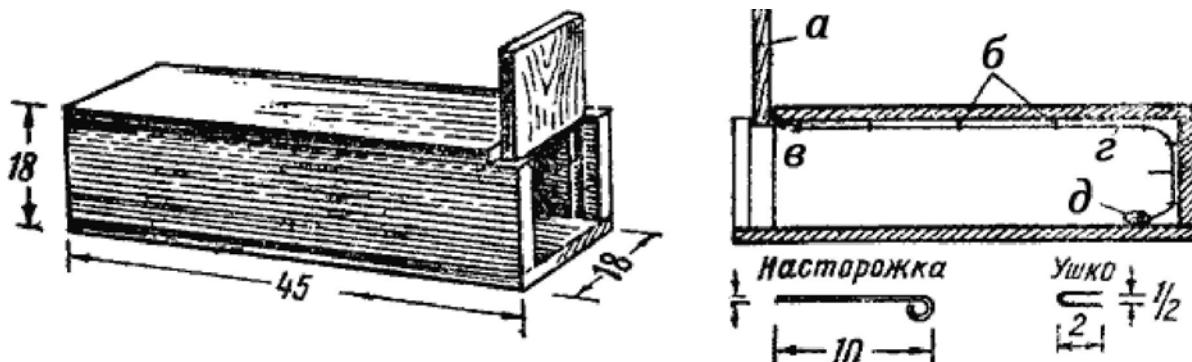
Ящичная ловушка на белку с падающей дверцей (размеры в см): а — падающая дверка; б — направляющие ушки; в — проволочная насторожка; г — веревка; д — приманка
